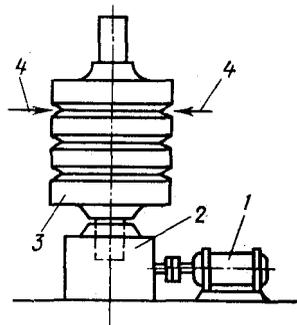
Схема сварки ротора газовой турбины
